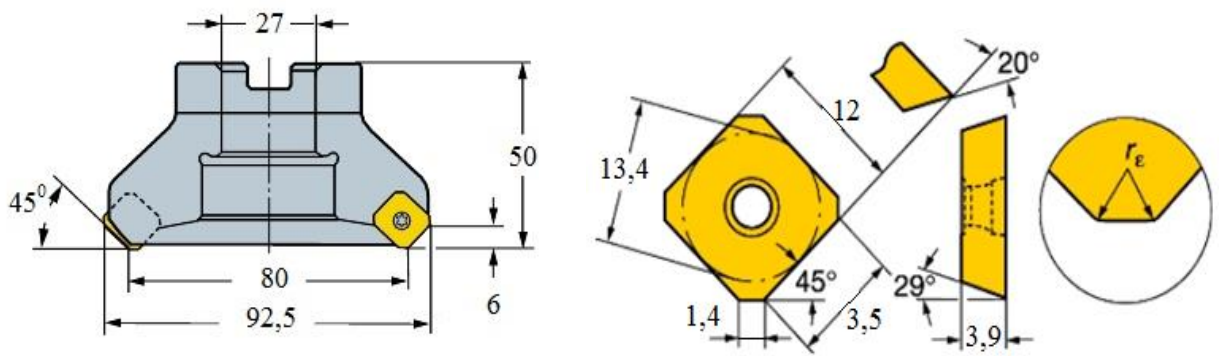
Фреза торцевая Ø80 CoroMill R245–080Q27–12M с пластинами 245R–1305
